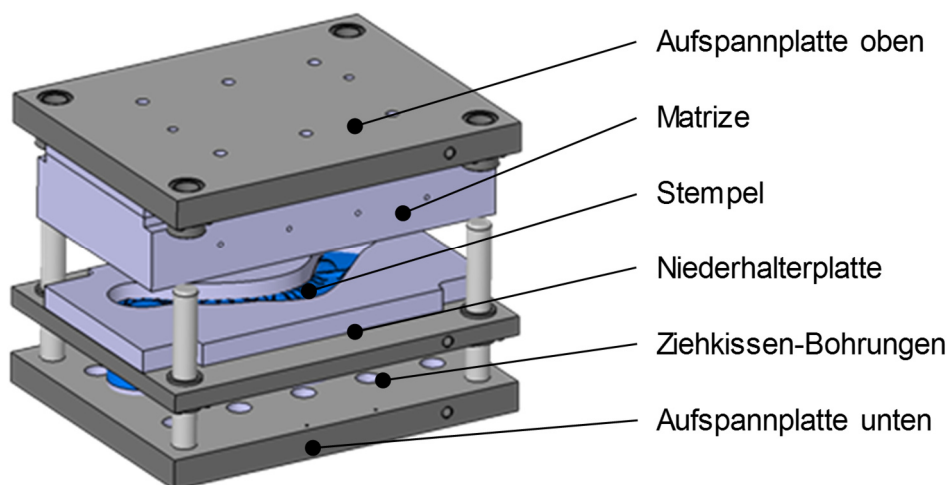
Werkzeuganordnung des Querlenker-Demonstrators
